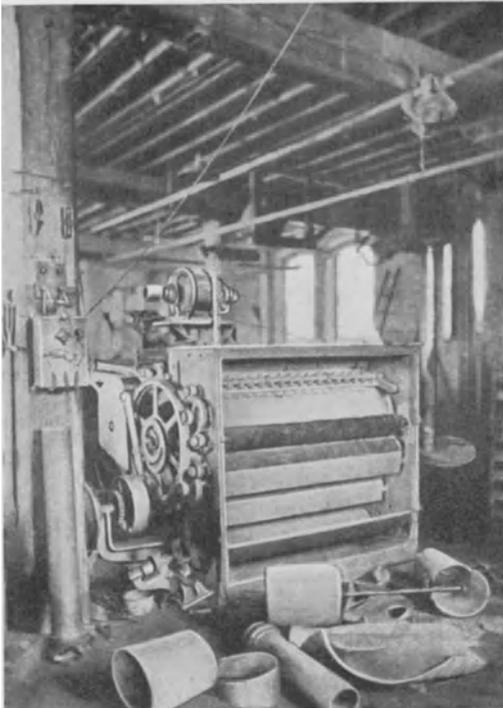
Nach der Staubexplosion in einer Etikettendruckmaschine.
